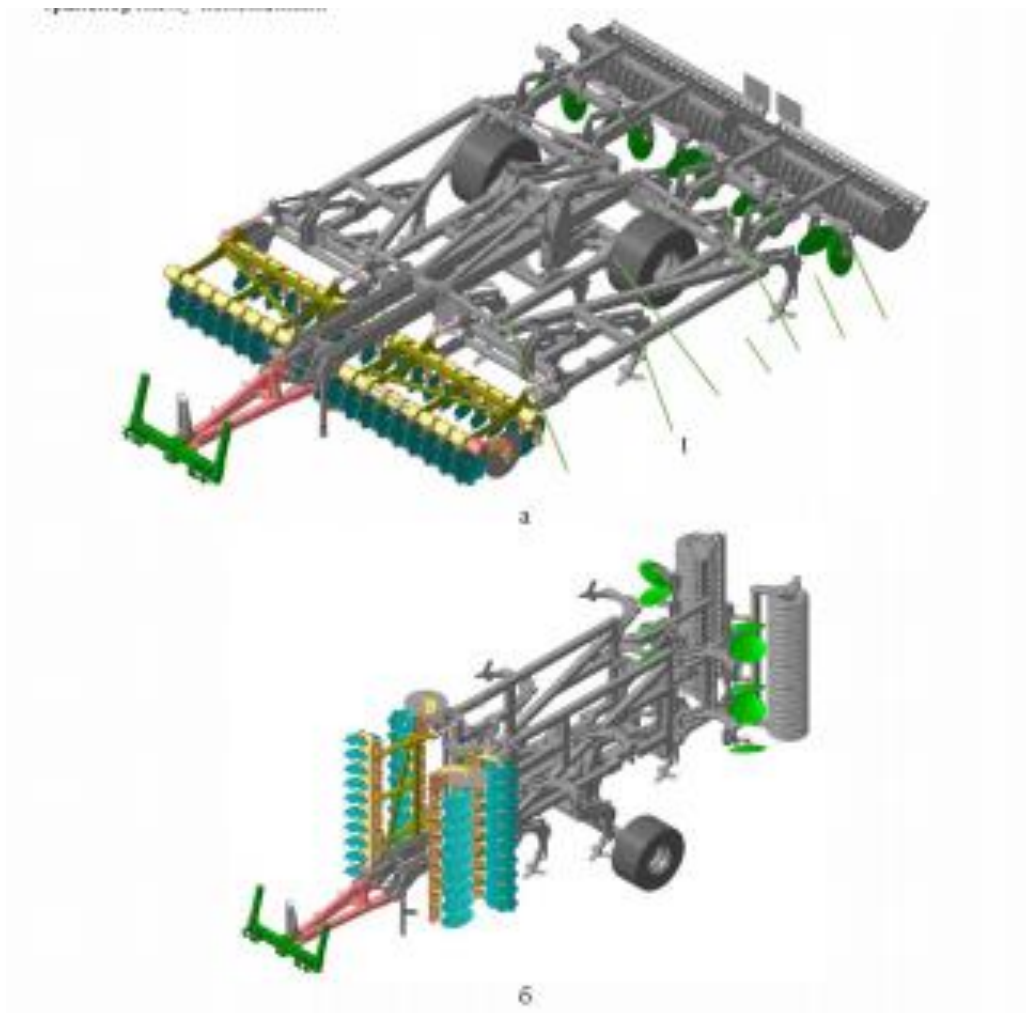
Розроблений ґрунтообробний широкозахватний агрегат АГШ у робочому (а) та транспортному (б) вигляді:
